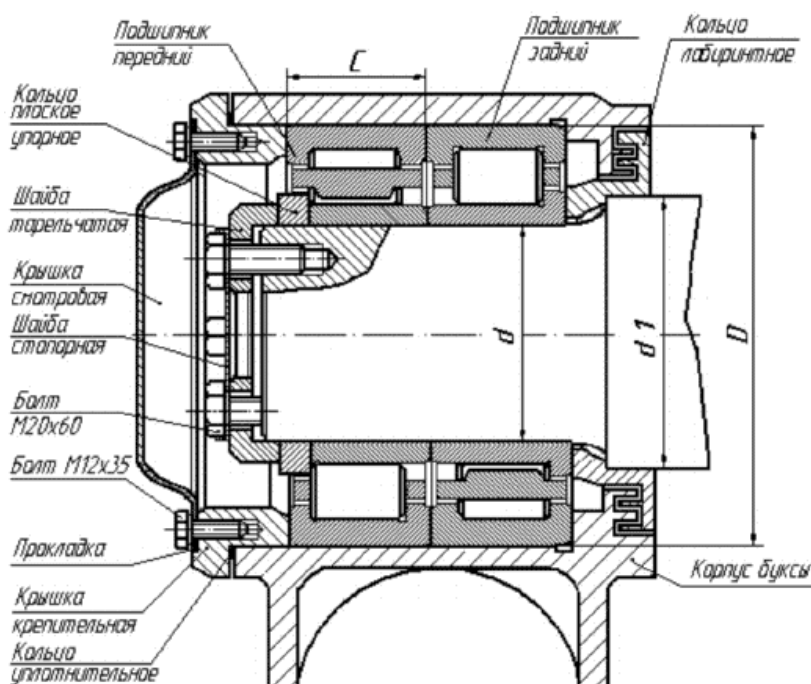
Буксовый узел с двумя подшипниками роликовыми цилиндрическими с торцевым креплением шайбой тарельчатой и болтами М20
